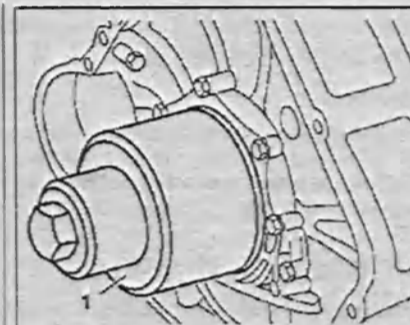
Запрессуйте сальник 21 в крышку до упора с помощью приспособления 1.
